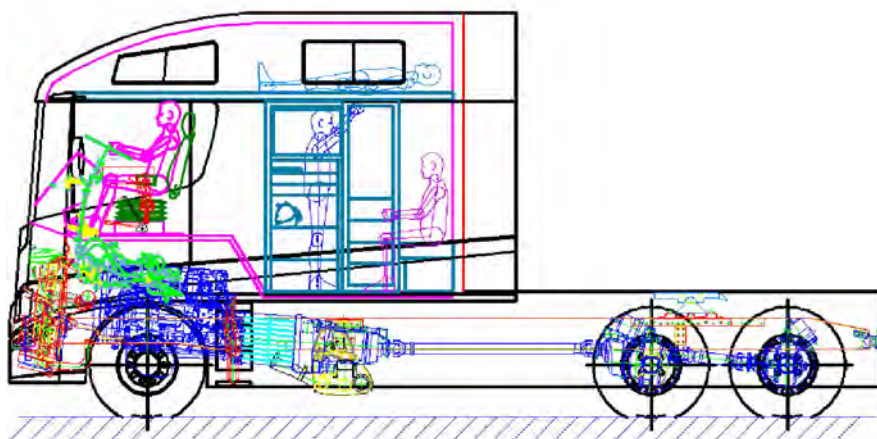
Компоновочный чертеж со схематически изображенными основными узлами и агрегатами
